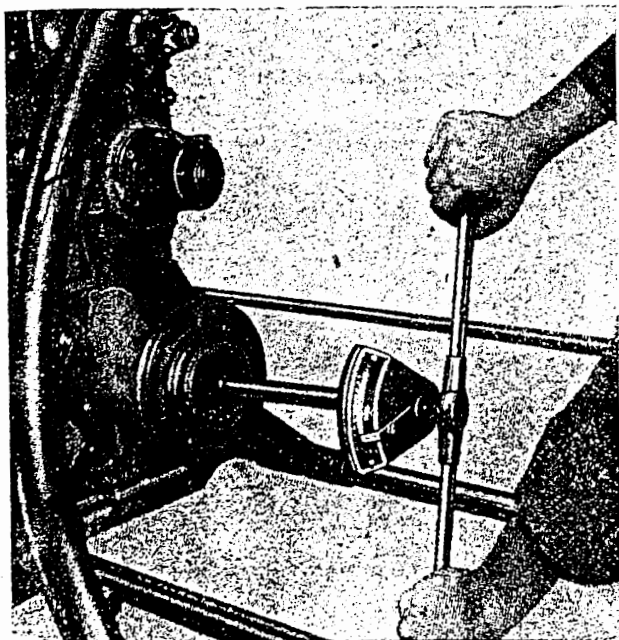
Befestigungsschrauben der Keilriemenscheibe mit Drehmomentschlüssel anziehen
